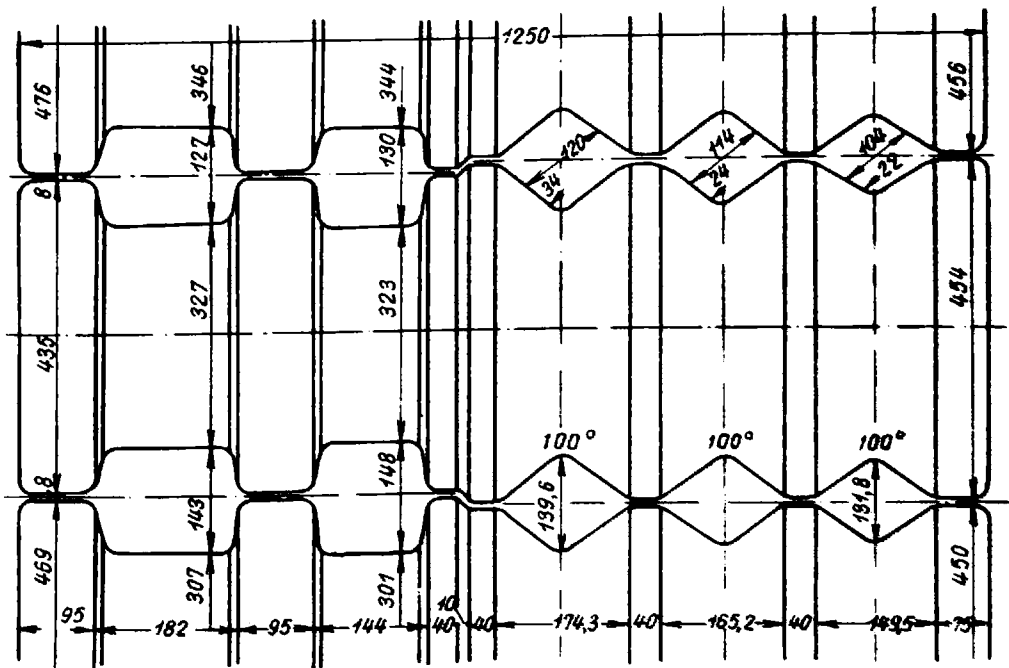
Валки с прямоугольными и ромбическими калибрами
